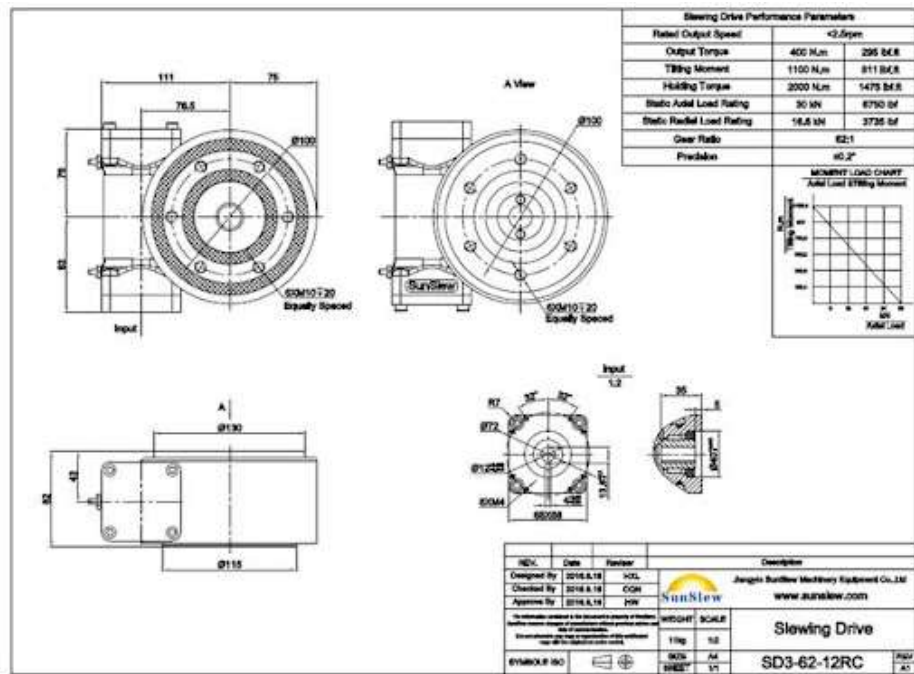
Схема одновісного черв'ячного редуктора
